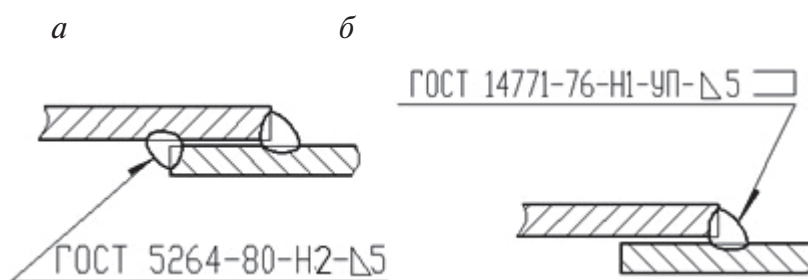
Примеры обозначения нахлесточного сварного шва:
